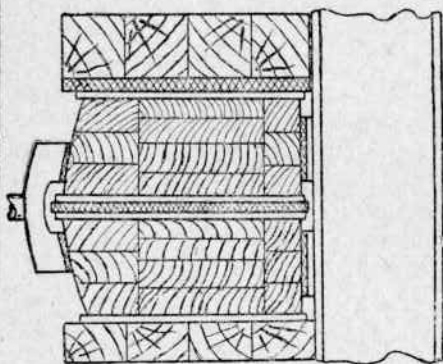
Шестисекционный пневматический шланговый пресс с вертикальным расположением секций для склейки полок лонжеронов.
